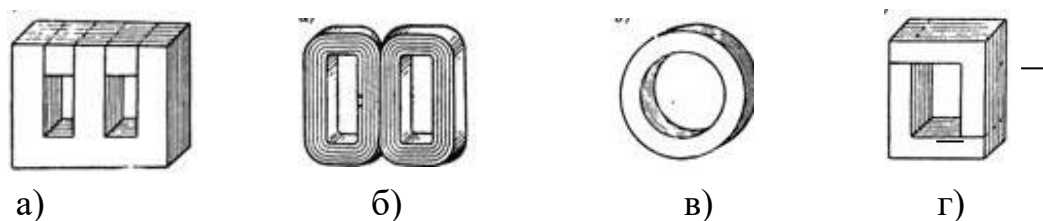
Конструкции сердечников трансформаторов: Ш-образный из пластин (а); из ленточных колец (б); прессованный (в) или стержневой (г)
